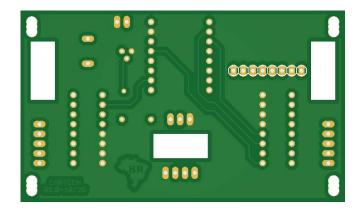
Placa CARTECH rev. 1.0 em tamanho real (lado da solda)
